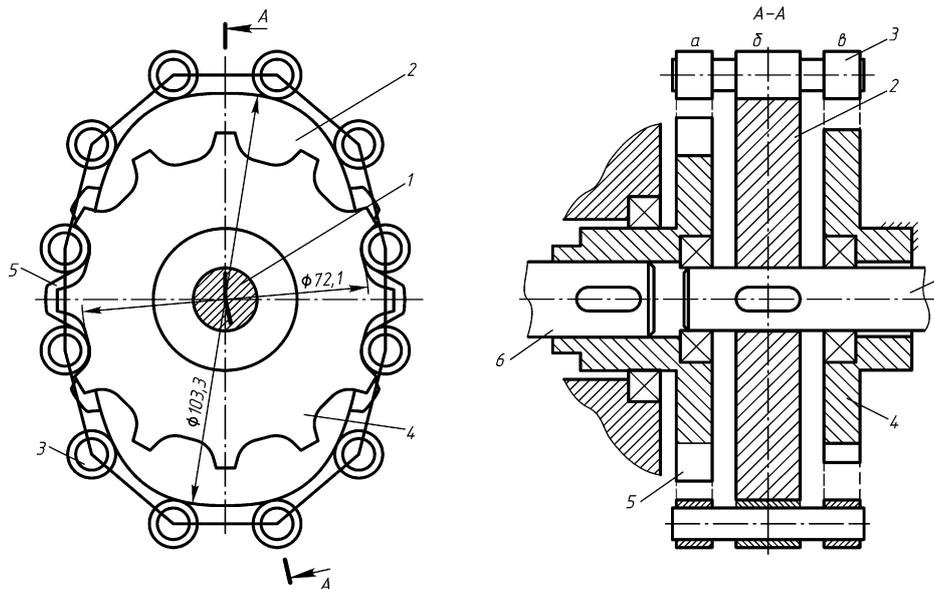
Конструктивная схема волновой зубчатой передачи с невращающейся втулочно-роликковой цепью: 1 – входной вал; 2 – генератор волн (кулачок); 3 – цепь; 4 – неподвижное зубчатое колесо; 5 – ведомое зубчатое колесо; 6 – выходной вал; а, в – ролики внешних рядов цепи; б – ролик внутреннего ряда цепи
